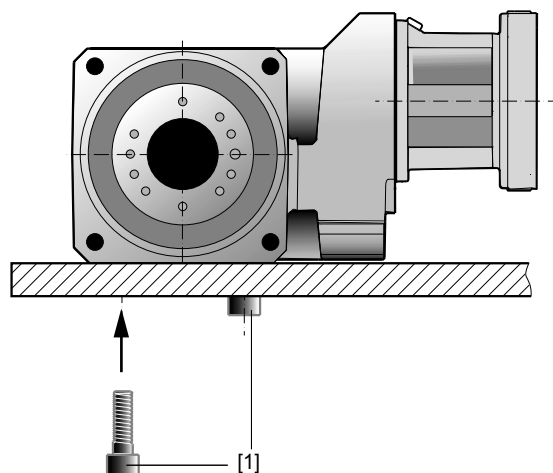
Крепление конического редуктора BSBF на опорную конструкцию установки с нижней стороны
